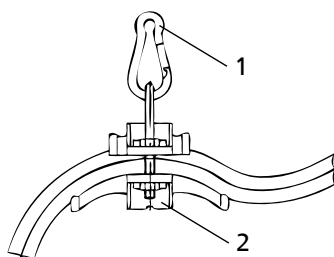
Fissaggio dei cavi di collegamento elettrici
